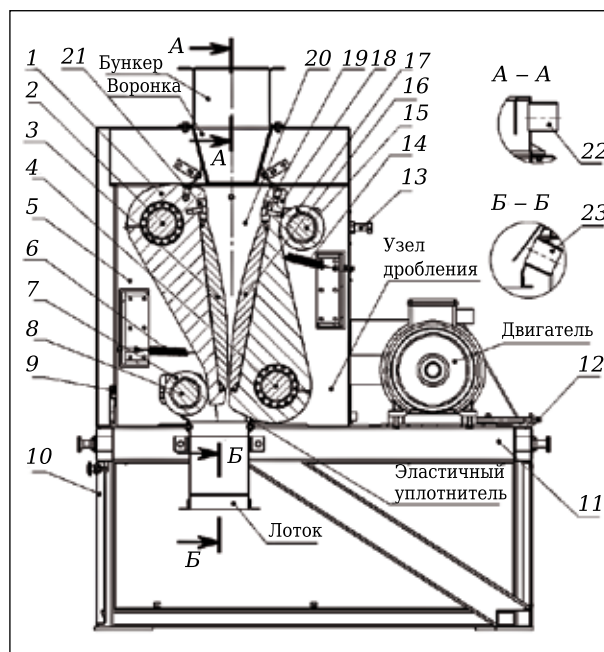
Щековая дробилка ЩДС-I-1,6×3,9 (разрез): 1 — шатун передний; 2, 4 — вал эксцентриковый; 3, 16 — щека; 5 — корпус; 6, 14 — пружина возвратная; 7, 17 — опора шатуна; 8, 15 — ось опоры; 9, 13 — болт; 10, 19 — стенка передняя; 11 — рама; 12 — шпилька натяжная; 18 — шатун задний; 19, 21 — планка прижимная; 20 — щека боковая; 22, 23 — патрубок
